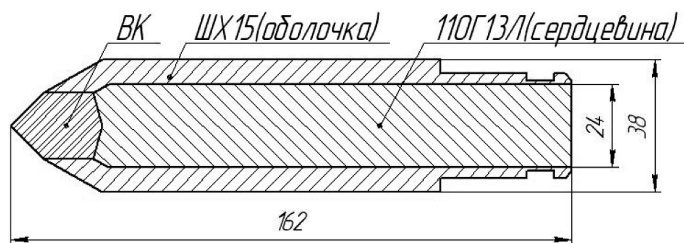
Схема реза РШ 38-75 с предлагаемой конструкцией биметаллического корпуса
